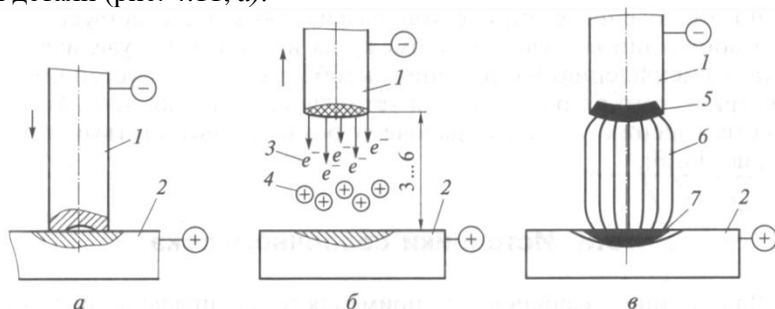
Схема зажигания электрической дуги: a — короткое замыкание; $б$ — ионизация воздушного промежутка за счет эмиссии электронов; $в$ — устойчивый дуговой разряд; 1 — электрод; 2 — свариваемая заготовка; 3 — электроны; 4 — ионы; 5 — зона плавления на катоде; 6 — электрическая дуга; 7 — зона плавления на аноде
